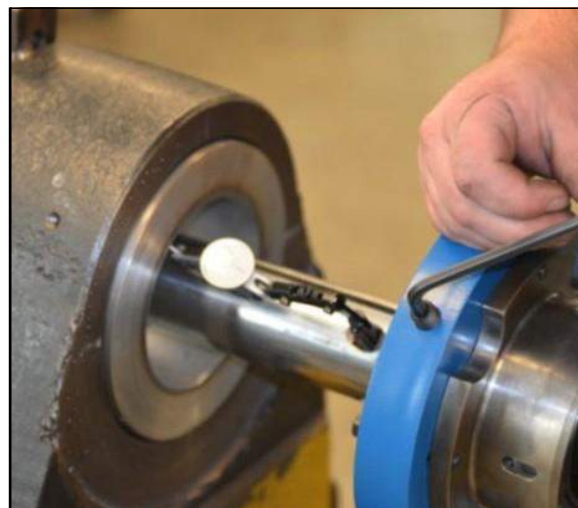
ALIGNEMENT DE LA BARRE
